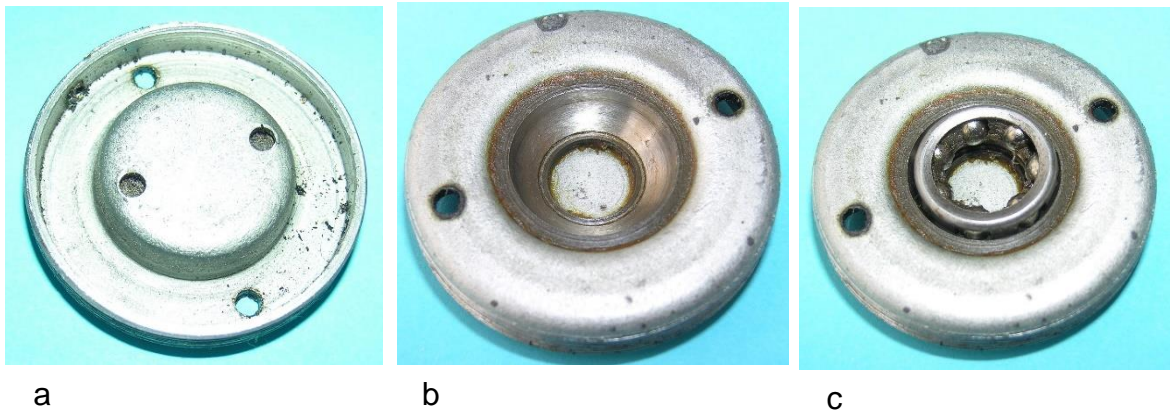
Boden: a) Boden mit zwei Montagebohrungen, b) Eingepresste Lagerschale, c) Eingelegtes Kugellager
